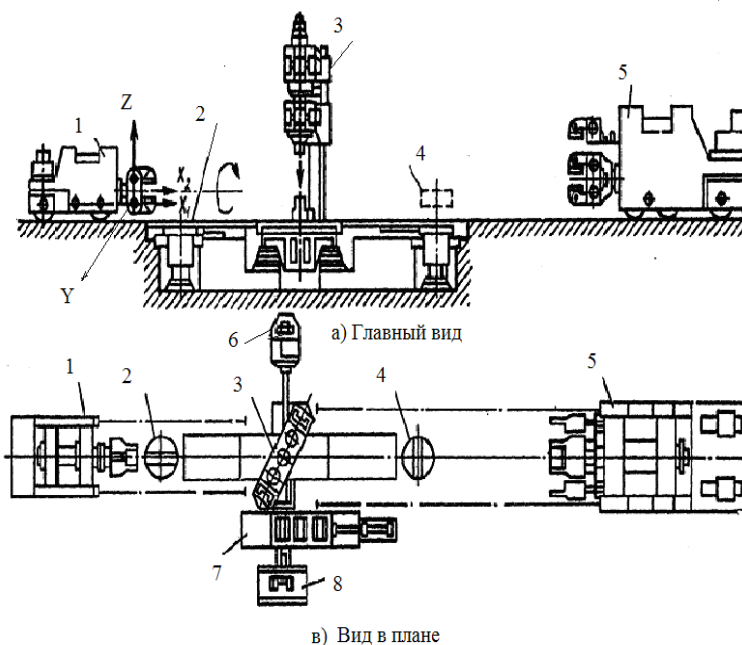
Компоновка роботизированного ковочного комплекса с программным управлением: 1 – манипулятор; 2, 4 – поворотные столы; 3 – ковочный пресс; 5 – ковочный манипулятор; 6 – инструментальный манипулятор; 7 – передвижной стол для бойков; 8 – пульт управления по основным технологическим перемещениям манипулятора с захватом в направлении осей X, Y, Z.
